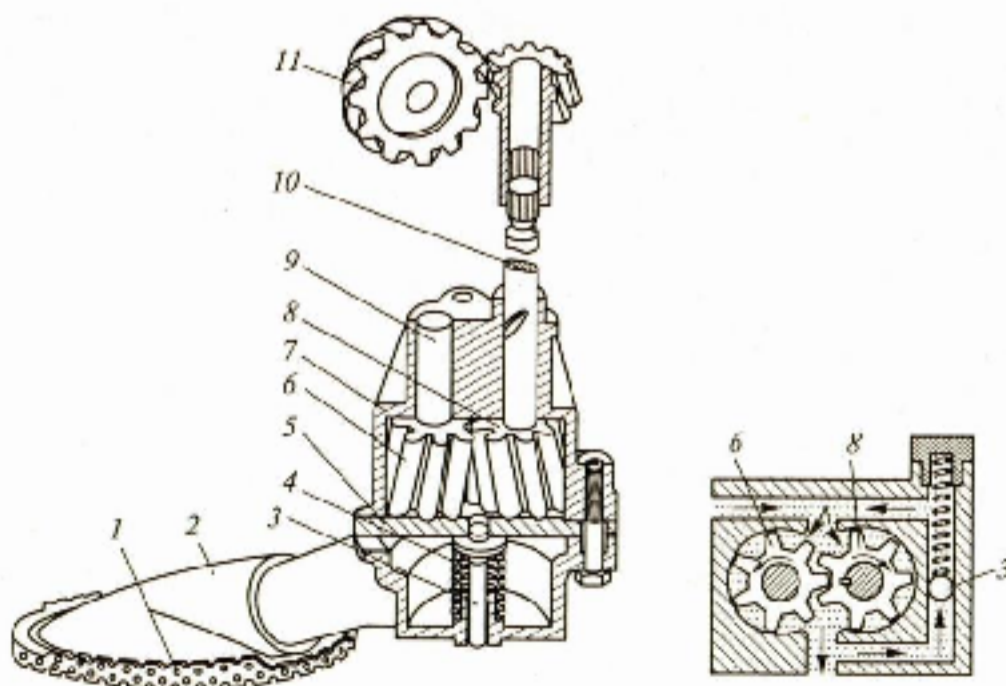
Устройство односекционного масляного насоса: 1-сетчатый фильтр; 2 -маслоприёмник; 3 -редукционный клапан; 4 -пружина клапана; 5 – проставка; 6 –ведомая шестерня; 7 -корпус; 8 -ведущая шестерня; 9 – ось ведомой шестерни; 10 --вал привода ведущей шестерни; 11 –шестерня привода вспомогательных механизмов
